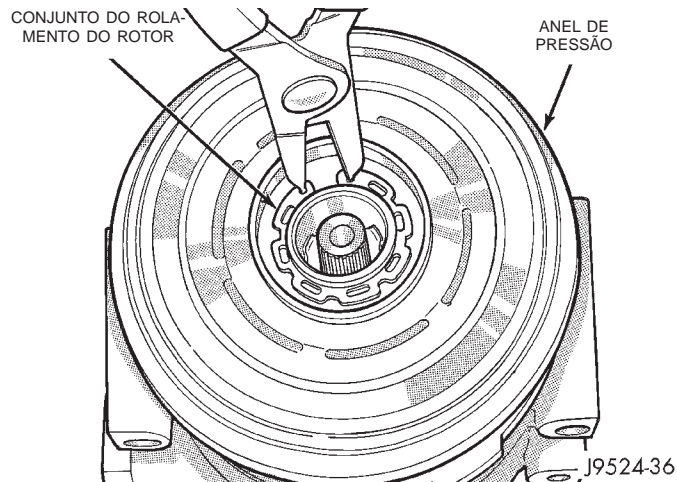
Remoção/Instalação do Anel de Pressão Externo
